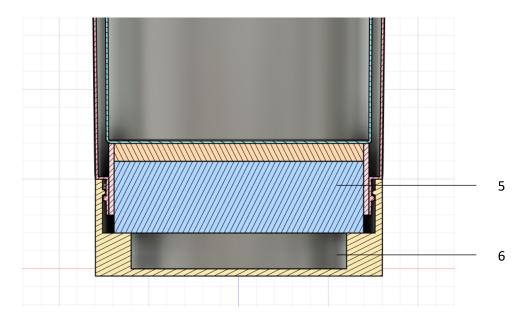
Detalle Tapa Peltier, Tapa-Peltier (6).
